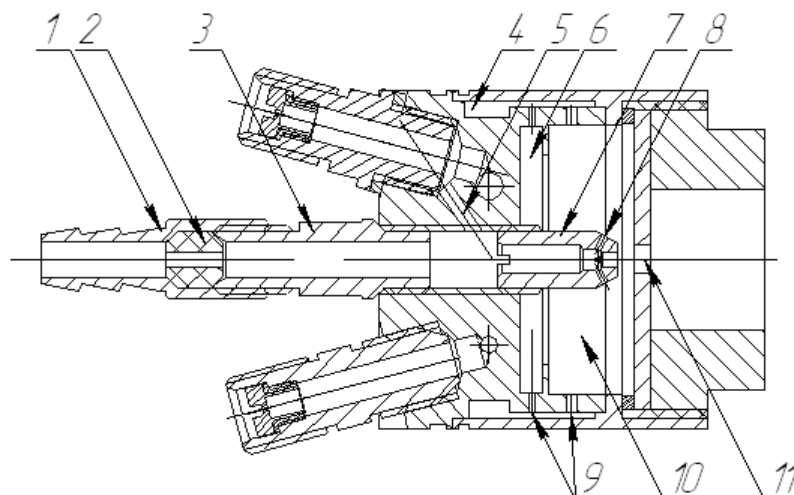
Опытный образец пропановоздушного проволочного металлатора ПВМ-1:
